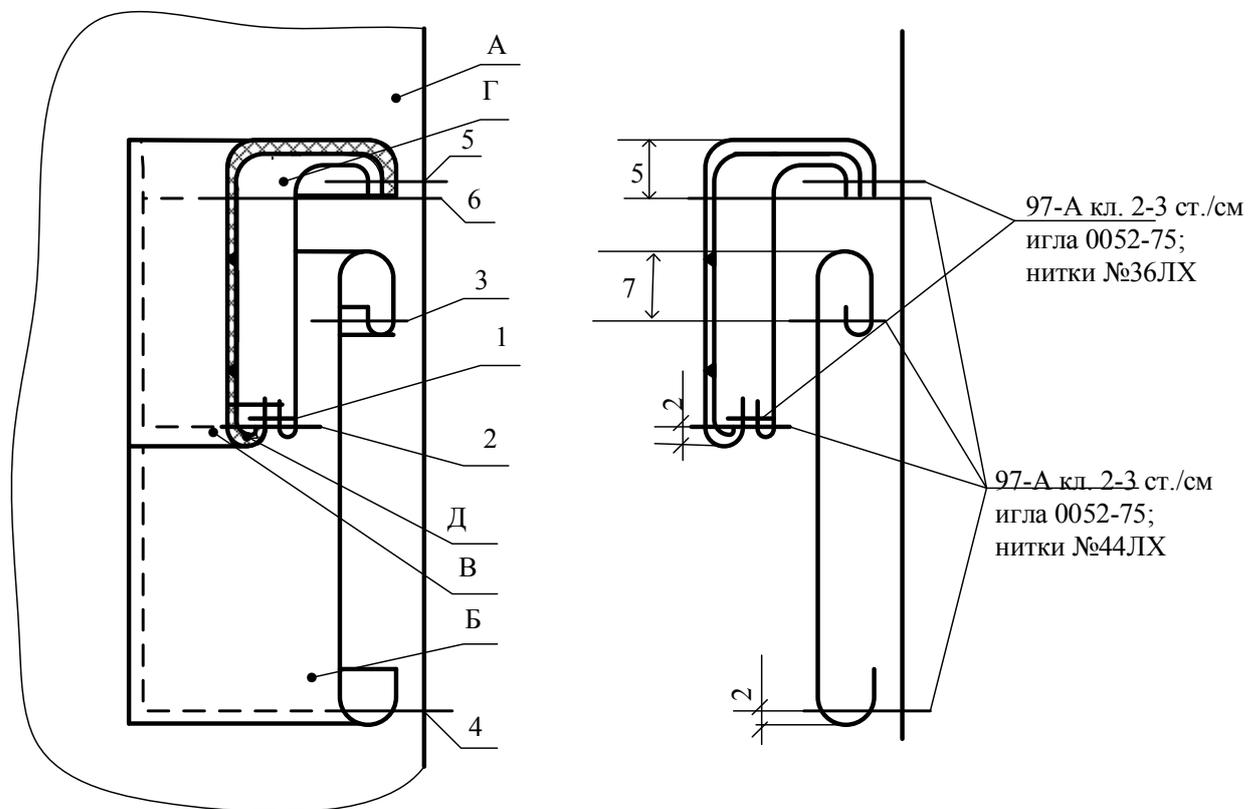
Чертеж МК рукава и воротника стойка
